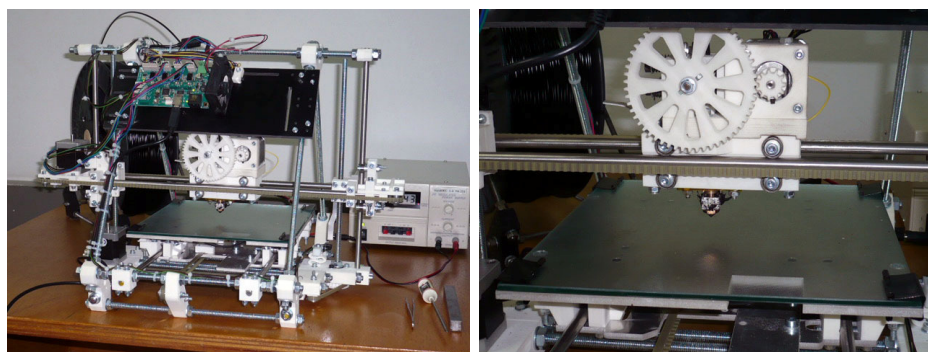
Máquina de fabricación por adición de los utillajes diseñados y detalle del extrusor
